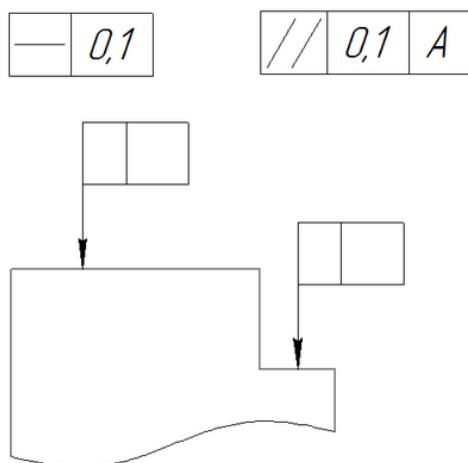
Нанесение обозначения допусков формы и расположения
